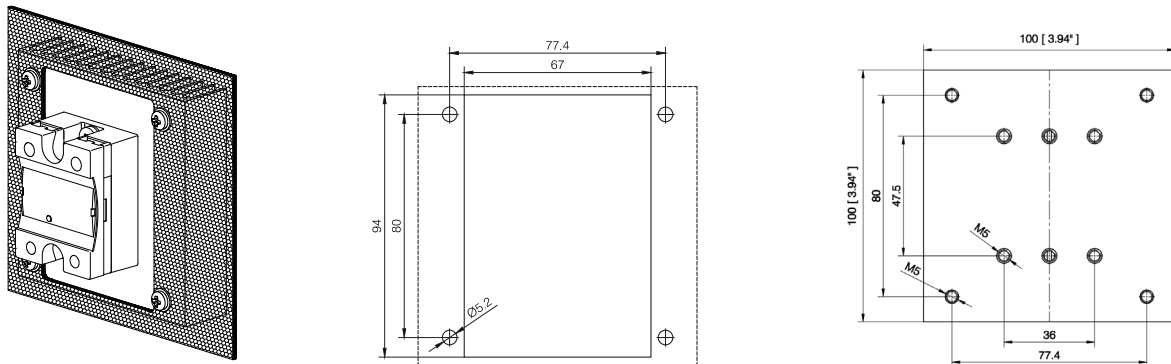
Position der Befestigungsbohrungen für die Montage durch die Schaltschrankrückwand.
